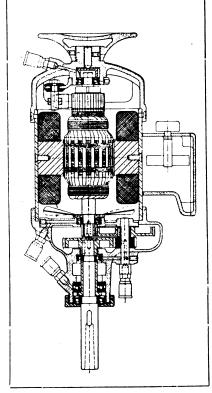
Schnitt durch eine elektrische Bohrmaschine.
